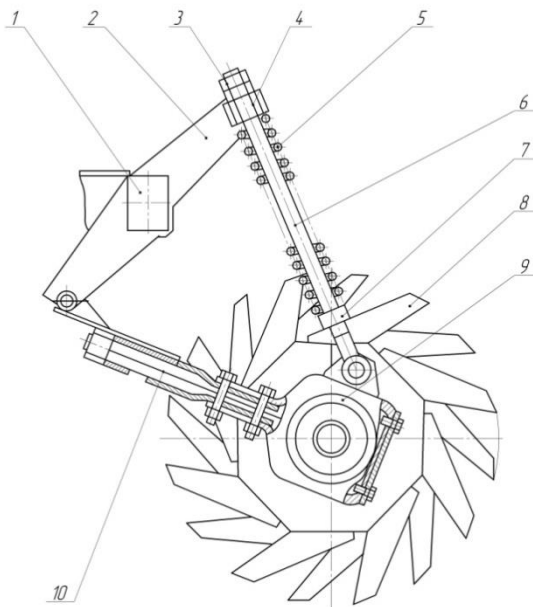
Фрезерное почвообрабатывающее орудие:
